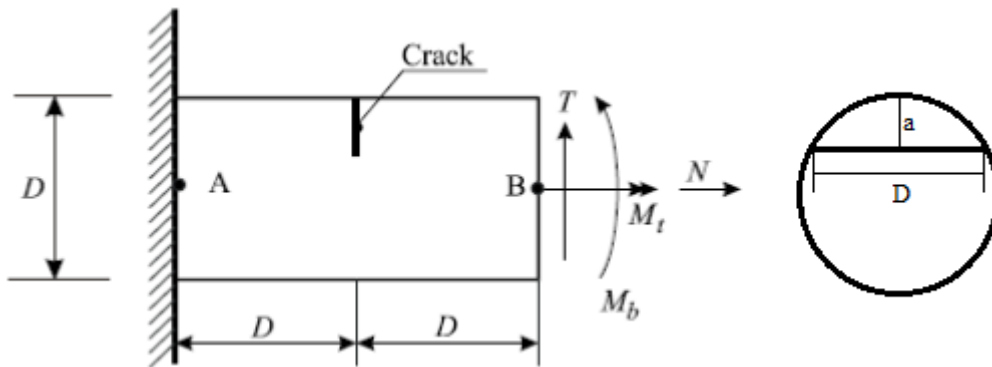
Eje empotrado y sección transversal de la fisura
